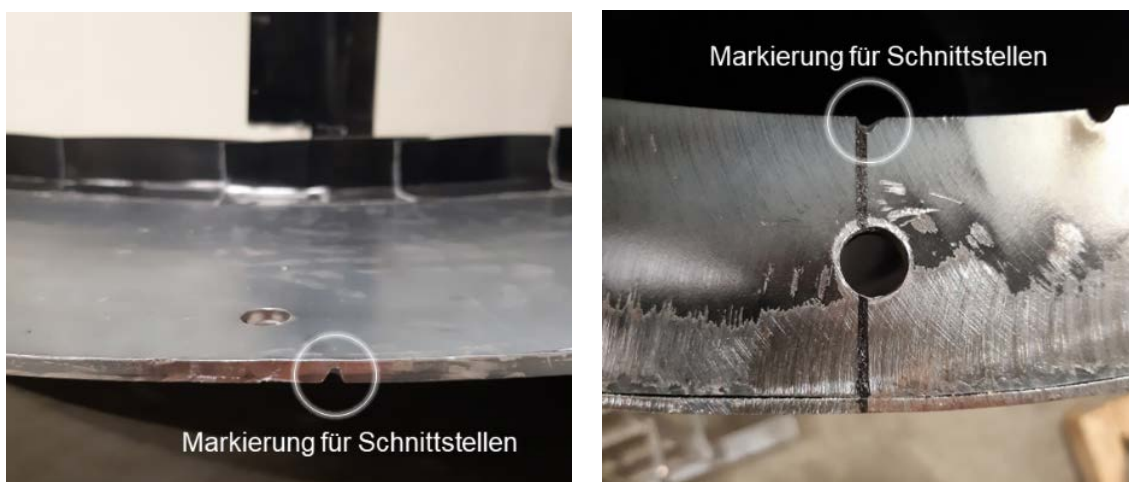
Schnittstellenmarkierung am Formwerkzeug. Links: untere Kreisplatte; rechts: angeschweißte Lasche am Innenzylinder oben
